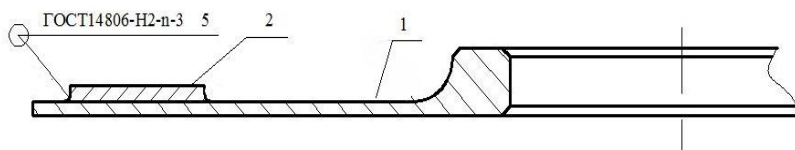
Эскиз предложенной конструкции заготовка гибкого колеса ТВЗП
